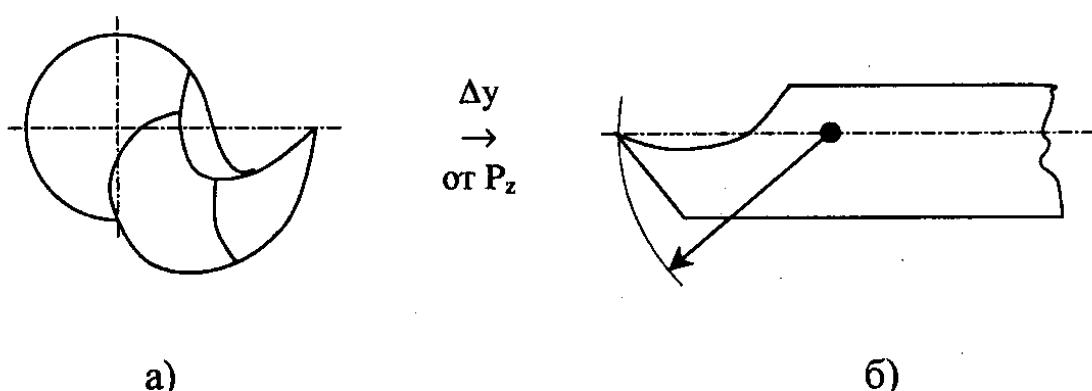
Конструкция резцов с низко расположенной режущей кромкой:
